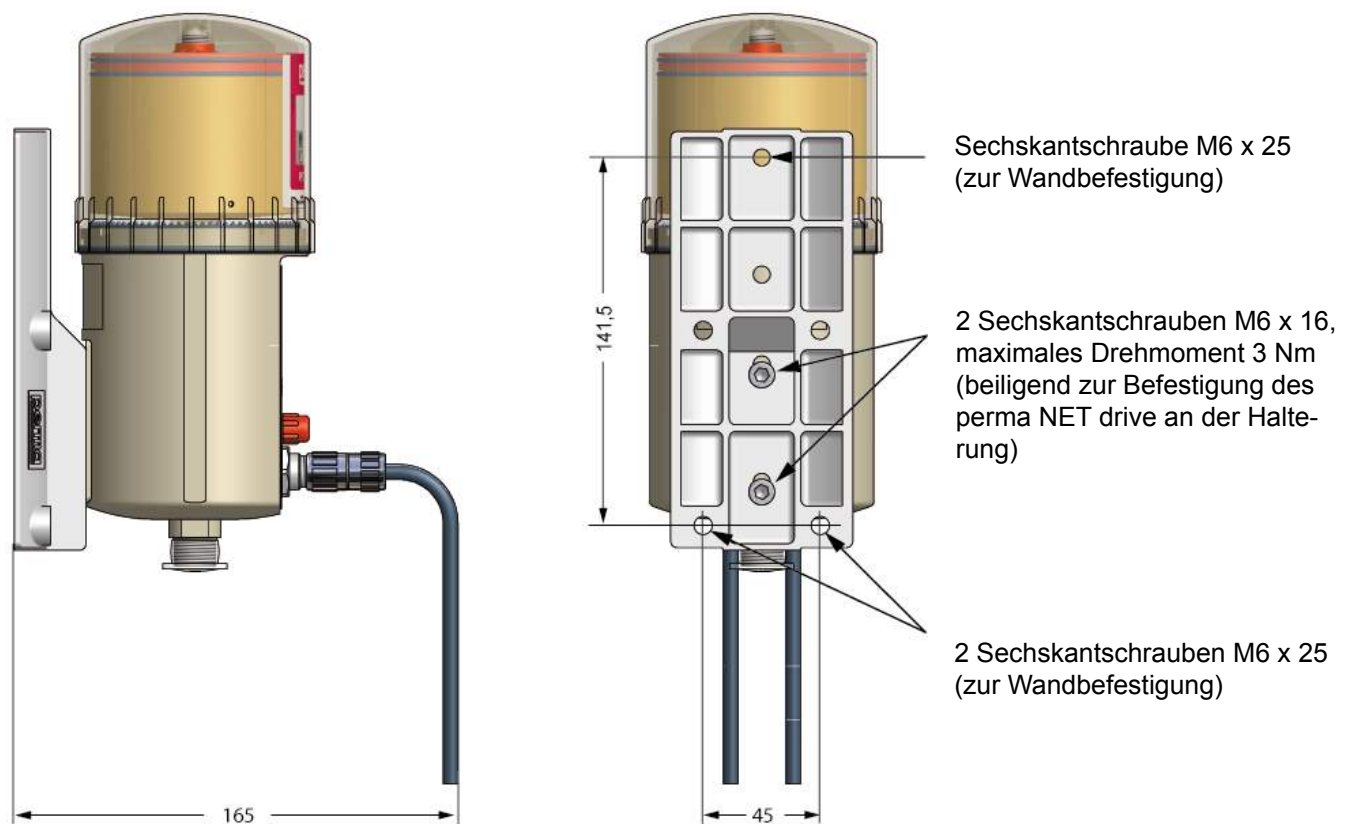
Bohrungsbild der drei Befestigungsschrauben
